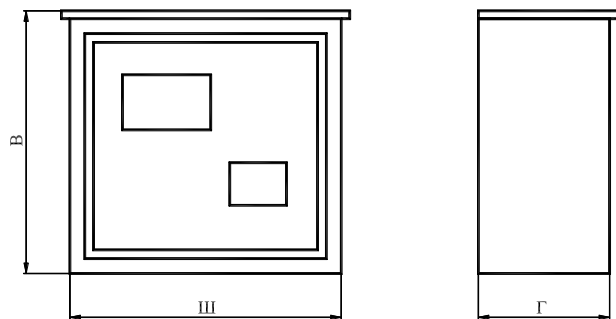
Габаритные размеры корпусов металлических ЩУ
